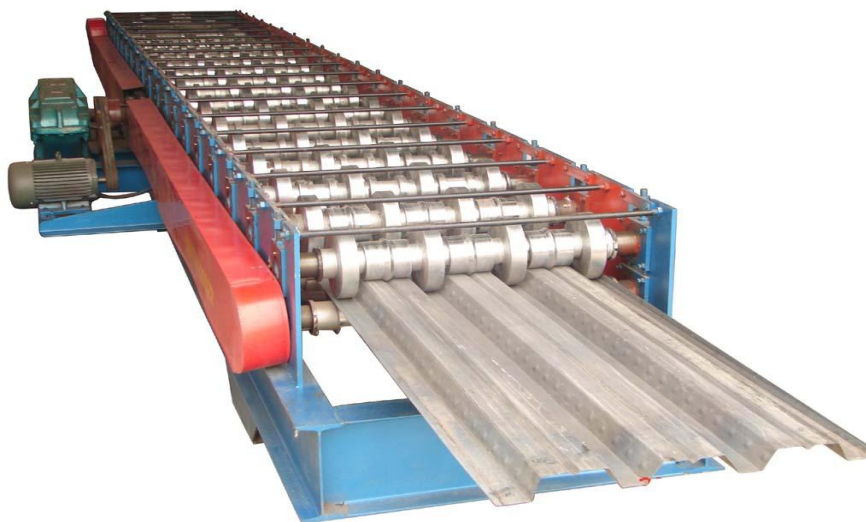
Máquina de laminagem a frio (Cold Roll Forming Machine (LM-688)) [31].
